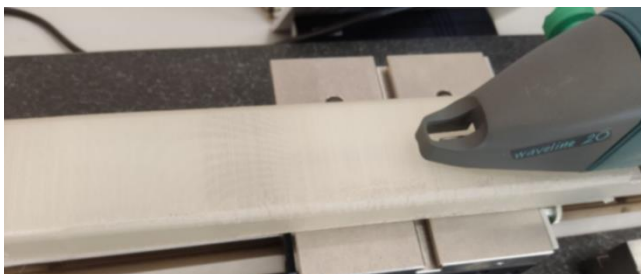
Процесс измерения шероховатости поверхности
